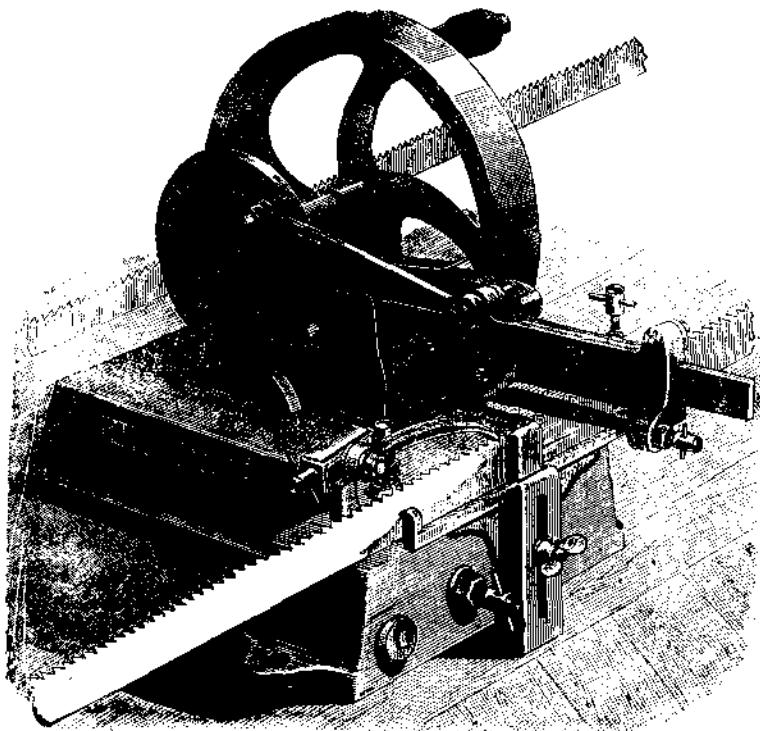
Станок для отточки зубьев ленточных пил с ручным приводом.
